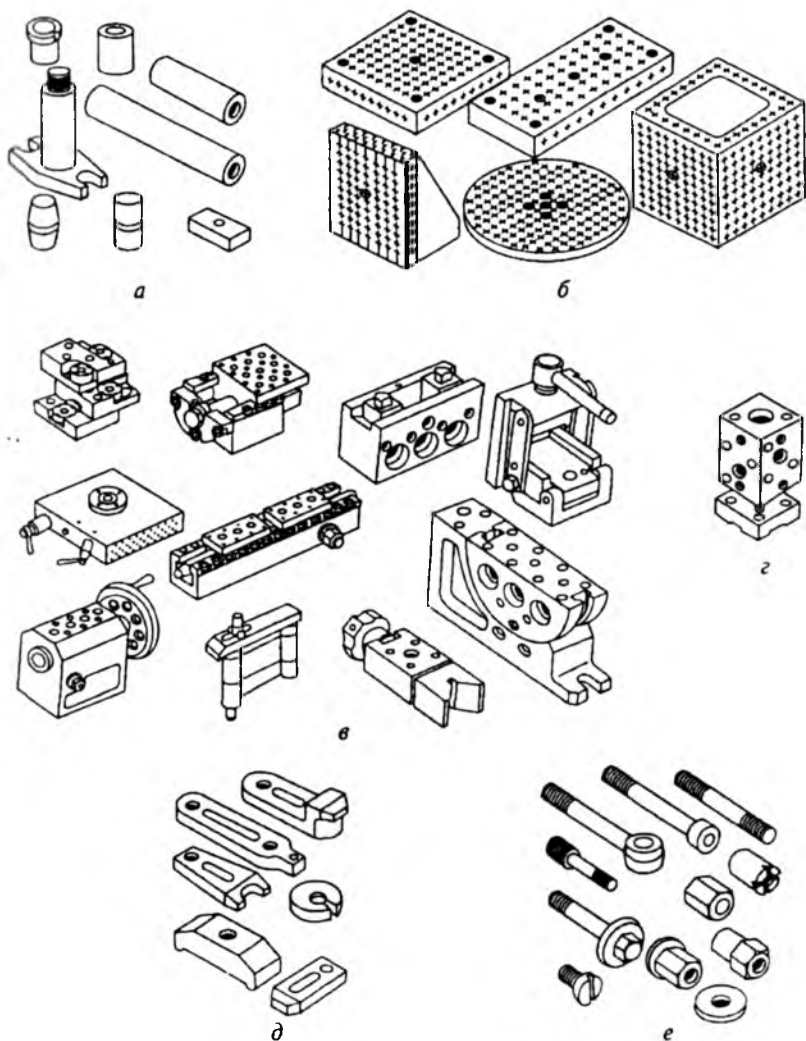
Базовый набор деталей и сборочных единиц универсально-сборочных приспособлений: а – проставки; б – плиты; в – различные механизмы; г – корпус; д – прихваты; е – элементы крепления
